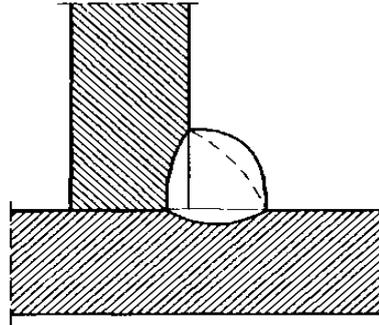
Превышение выпуклости таврового сварного шва (одностороннего)
